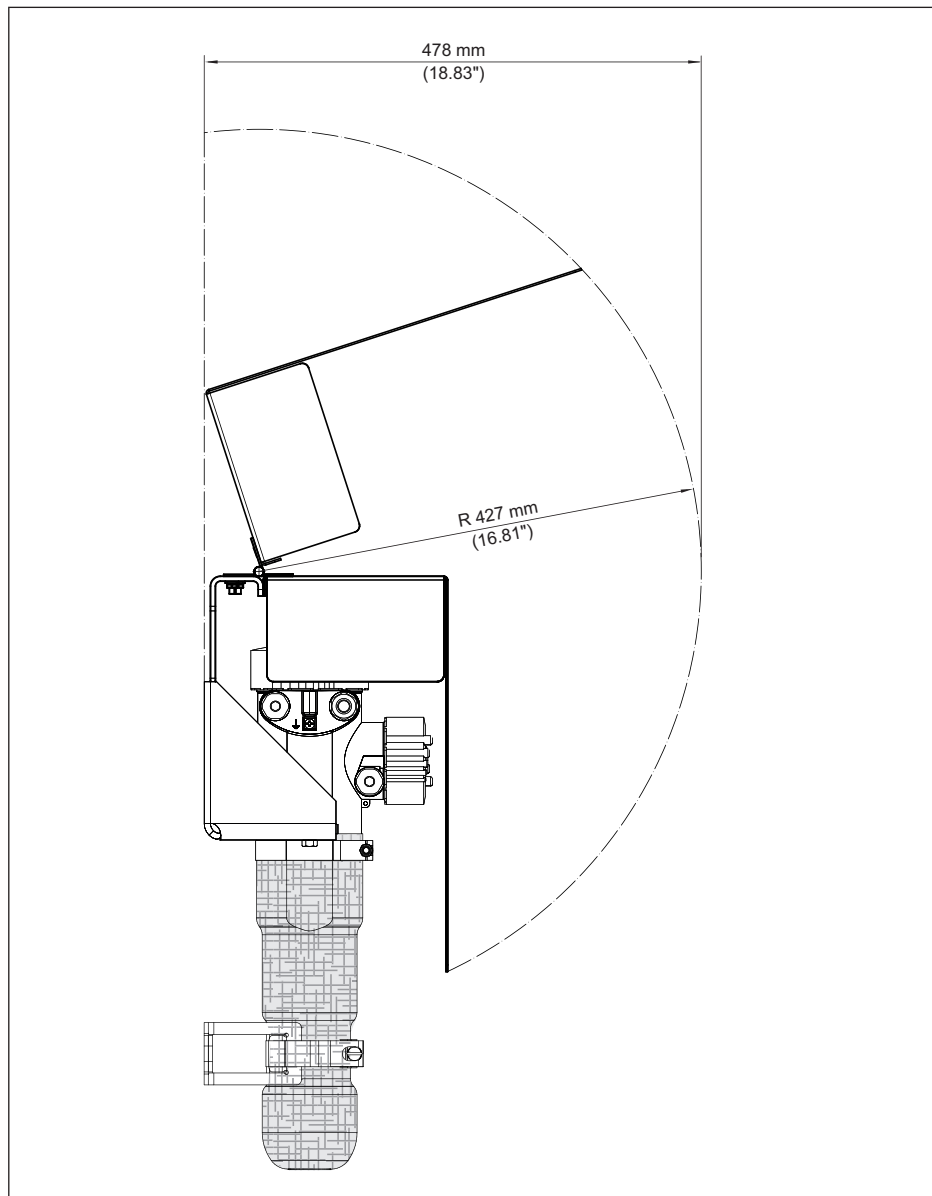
Protezione solare passiva con sensore montato verticalmente (area di apertura e servizio)
